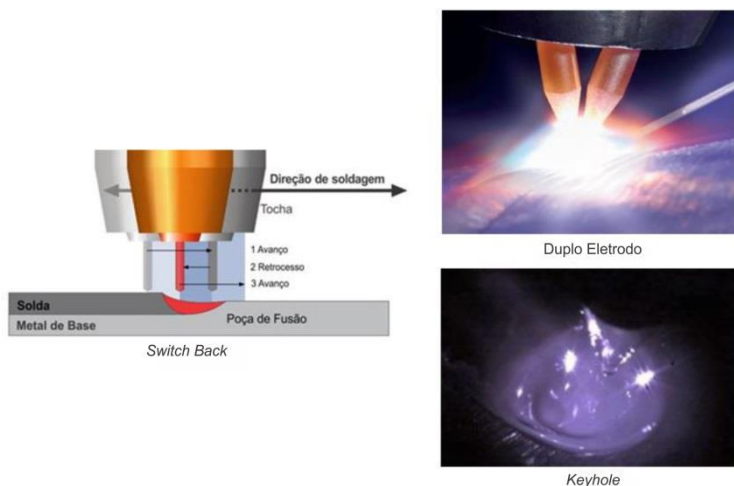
Técnicas de soldagem do processo TIG que visam o aumento da produtividade [24][25][26].
